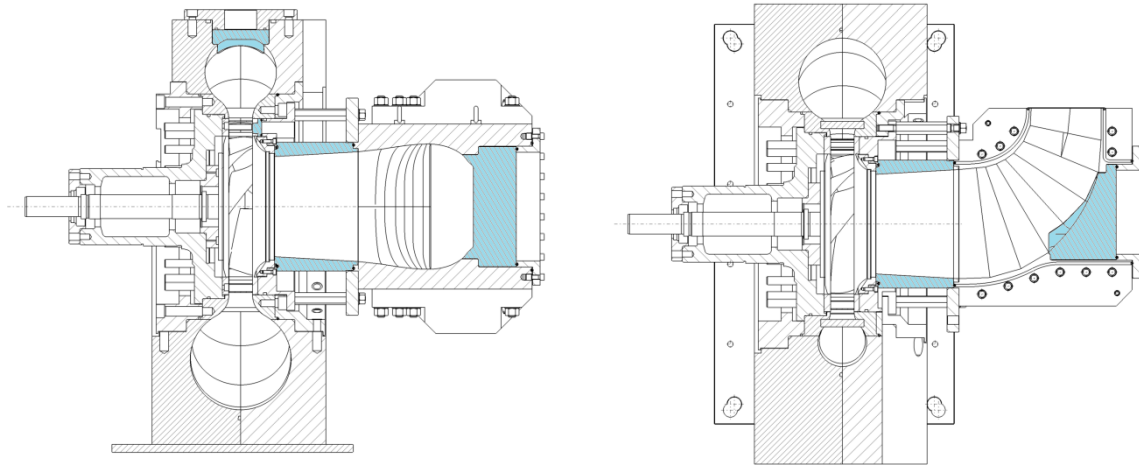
Ansichten Modellturbine mit Sichtfenster: Aufriss links und Grundriss rechts
